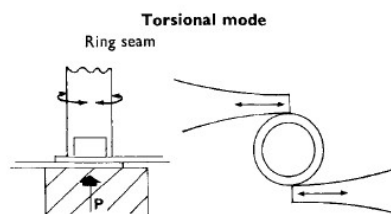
Torsionsschweißprozess (links) und Torsionsschwingungserzeugung durch tangentielle Ankopplung von Längsschwingern (rechts). Quelle: E.A. Neppiras, „Ultrasonic Welding of Metals“, Ultrasonics (1965)
